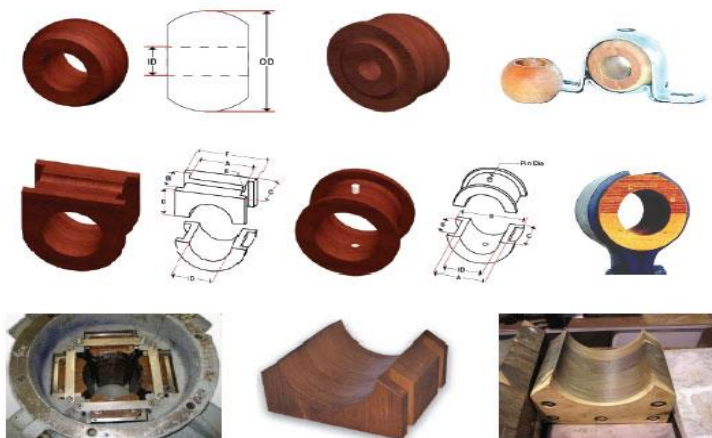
образцы подшипников, изготовленных из модифицированной древесины
